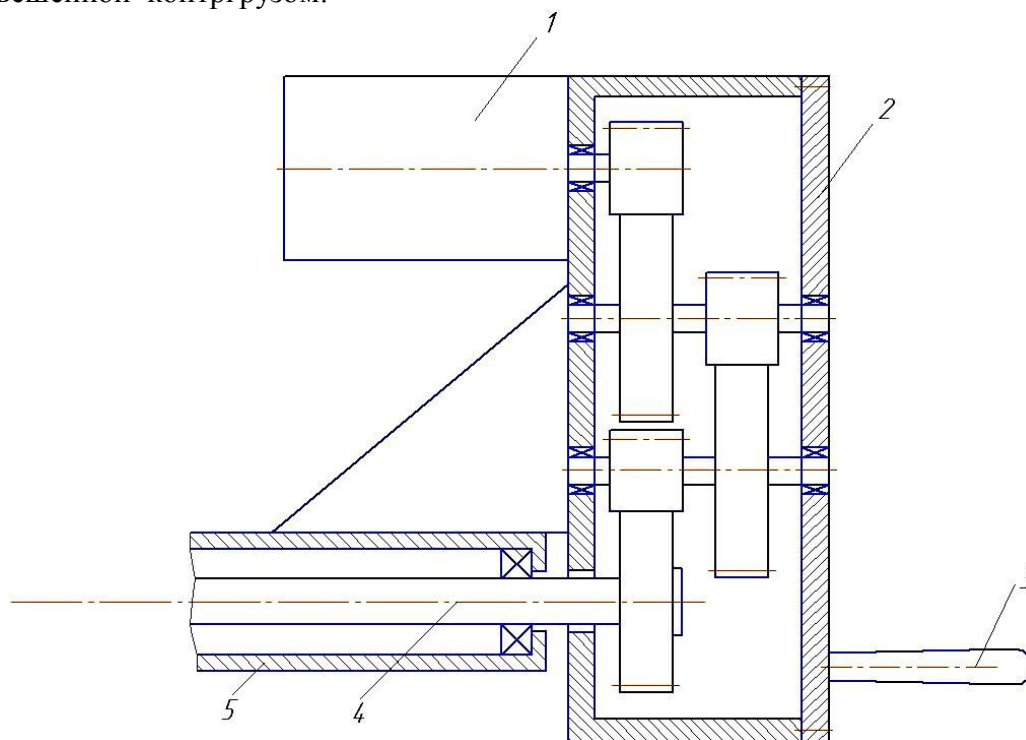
Схема электромеханического привода механизма поворота штанги: 1 – электродвигатель постоянного тока; 2 – вертикальный трехступенчатый редуктор; 3 – рукоятка; 4 – хвостовик поворотной штанги; 5 – мундштук
